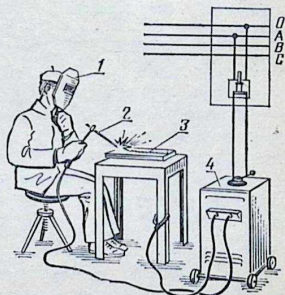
Пост ручной дуговой сварки:
